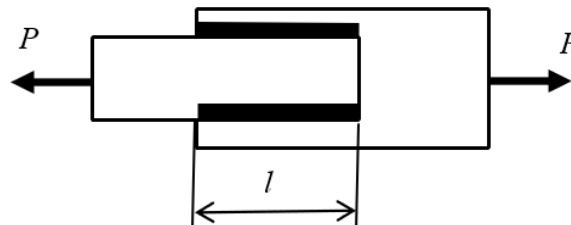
Схема сварного соединения внахлестку фланговыми швами
